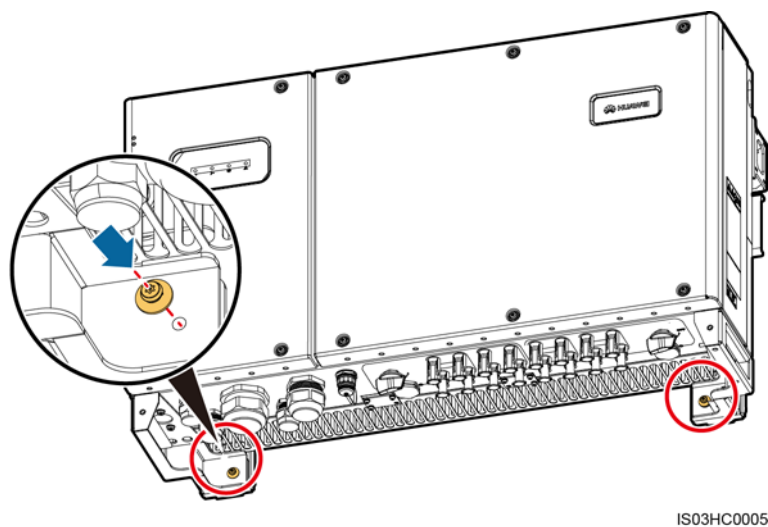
De SUN2000 op de montagesteun installeren.
